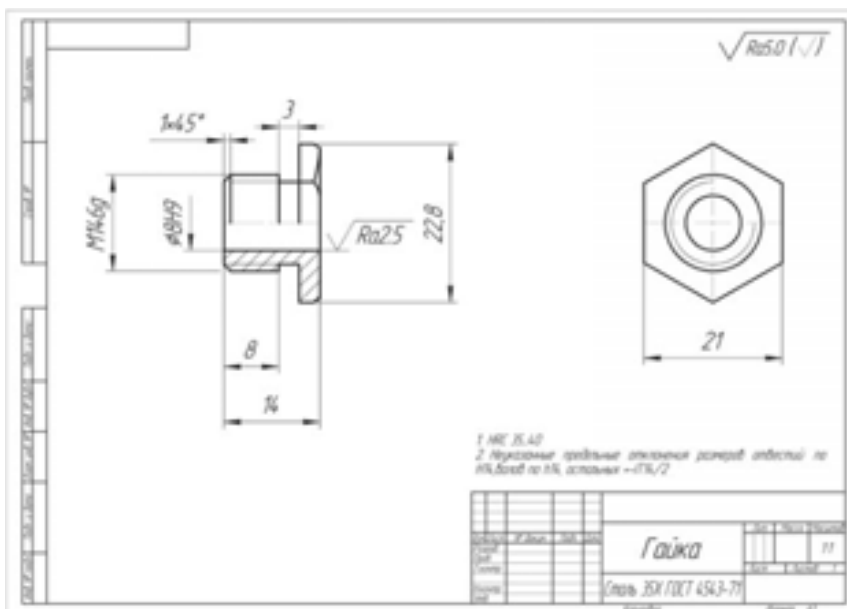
Окончательный вариант рабочего чертежа детали «Гайка»
